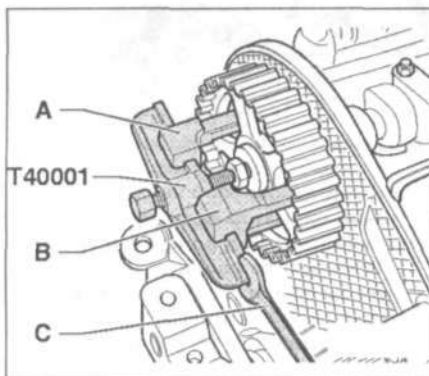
Ослабьте болт крепления шкива распределительного вала на полный оборот. Отсоедините шкив от ступицы с помощью приспособления Т40001.
